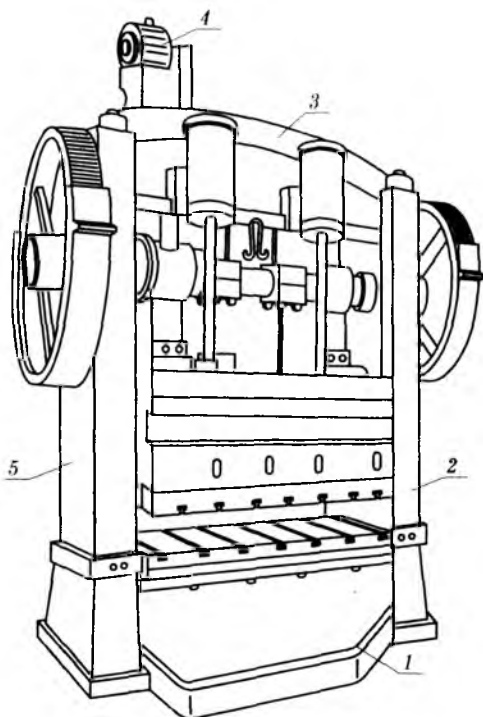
Двухстоечный кривошипный пресс простого действия для холодной листовой штамповки:
